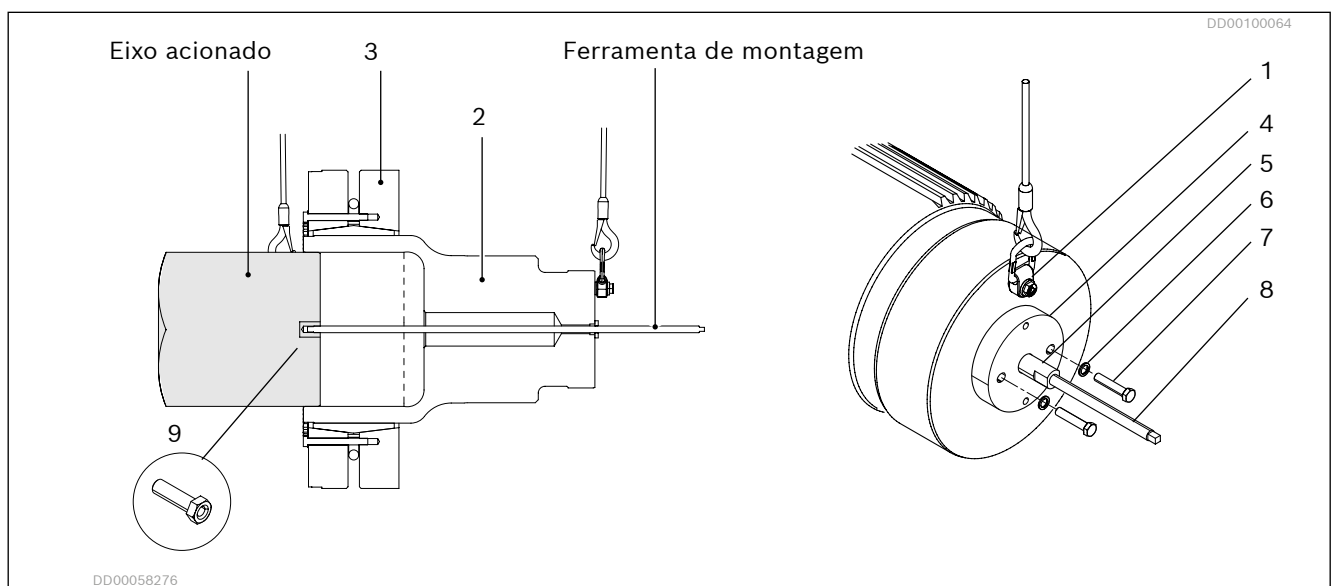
Montagem do adaptador de acoplamento com a ferramenta de montagem para CBp 280 a CBp 840
